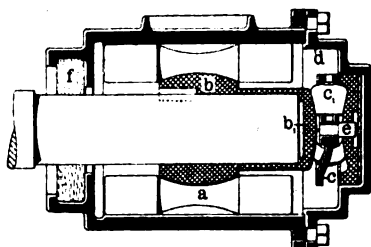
Rollenlager der Roller Bearing Truck Company Corporation in New York.
